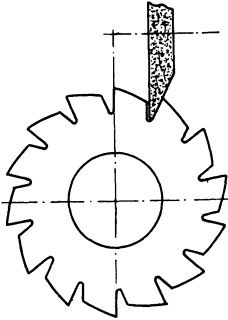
Das Schleifen hinterdrehter Fräser an der Zahnbrust.
